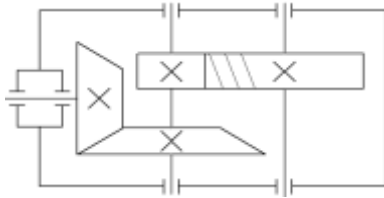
Кинематическая схема коническо-цилиндрического зубчатого редуктора
